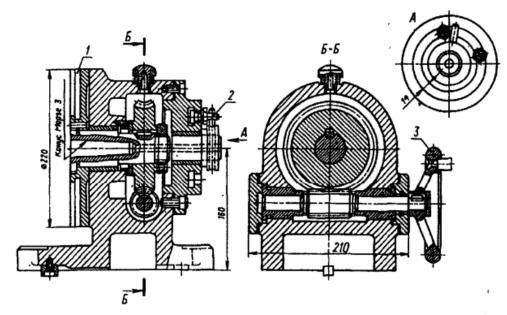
Поворотный стол для фрезеровани по радиусу
